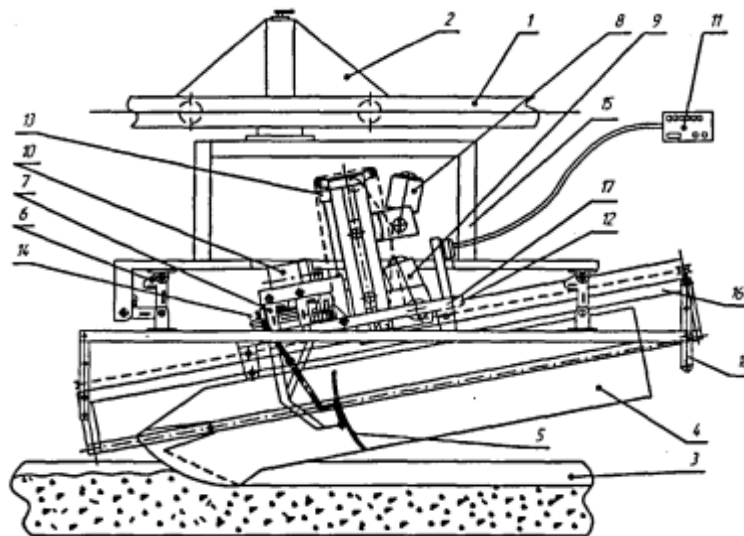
Конструктивна схема вимірювального ковша скрепера
